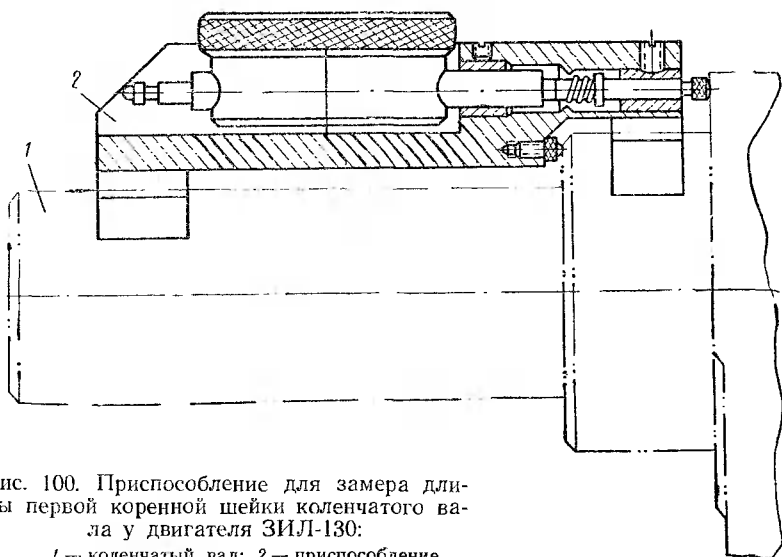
Приспособление для замера длины первой коренной шейки коленчатого вала у двигателя ЗИЛ-130:
